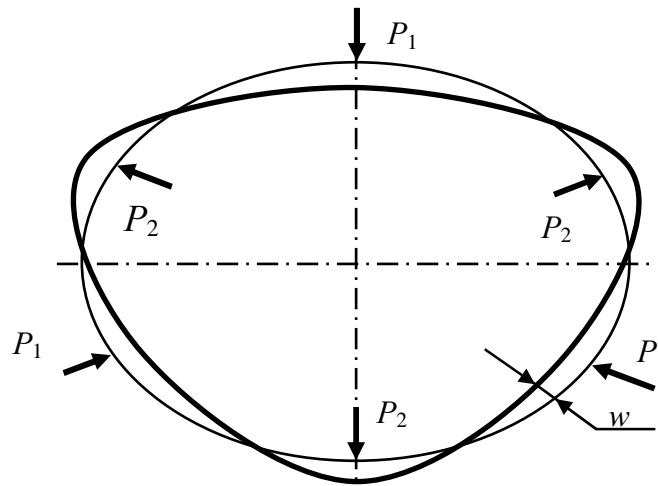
Схемы деформаций колец при механической обработке внутренней поверхности в трёхкулачковом зажимном устройстве
